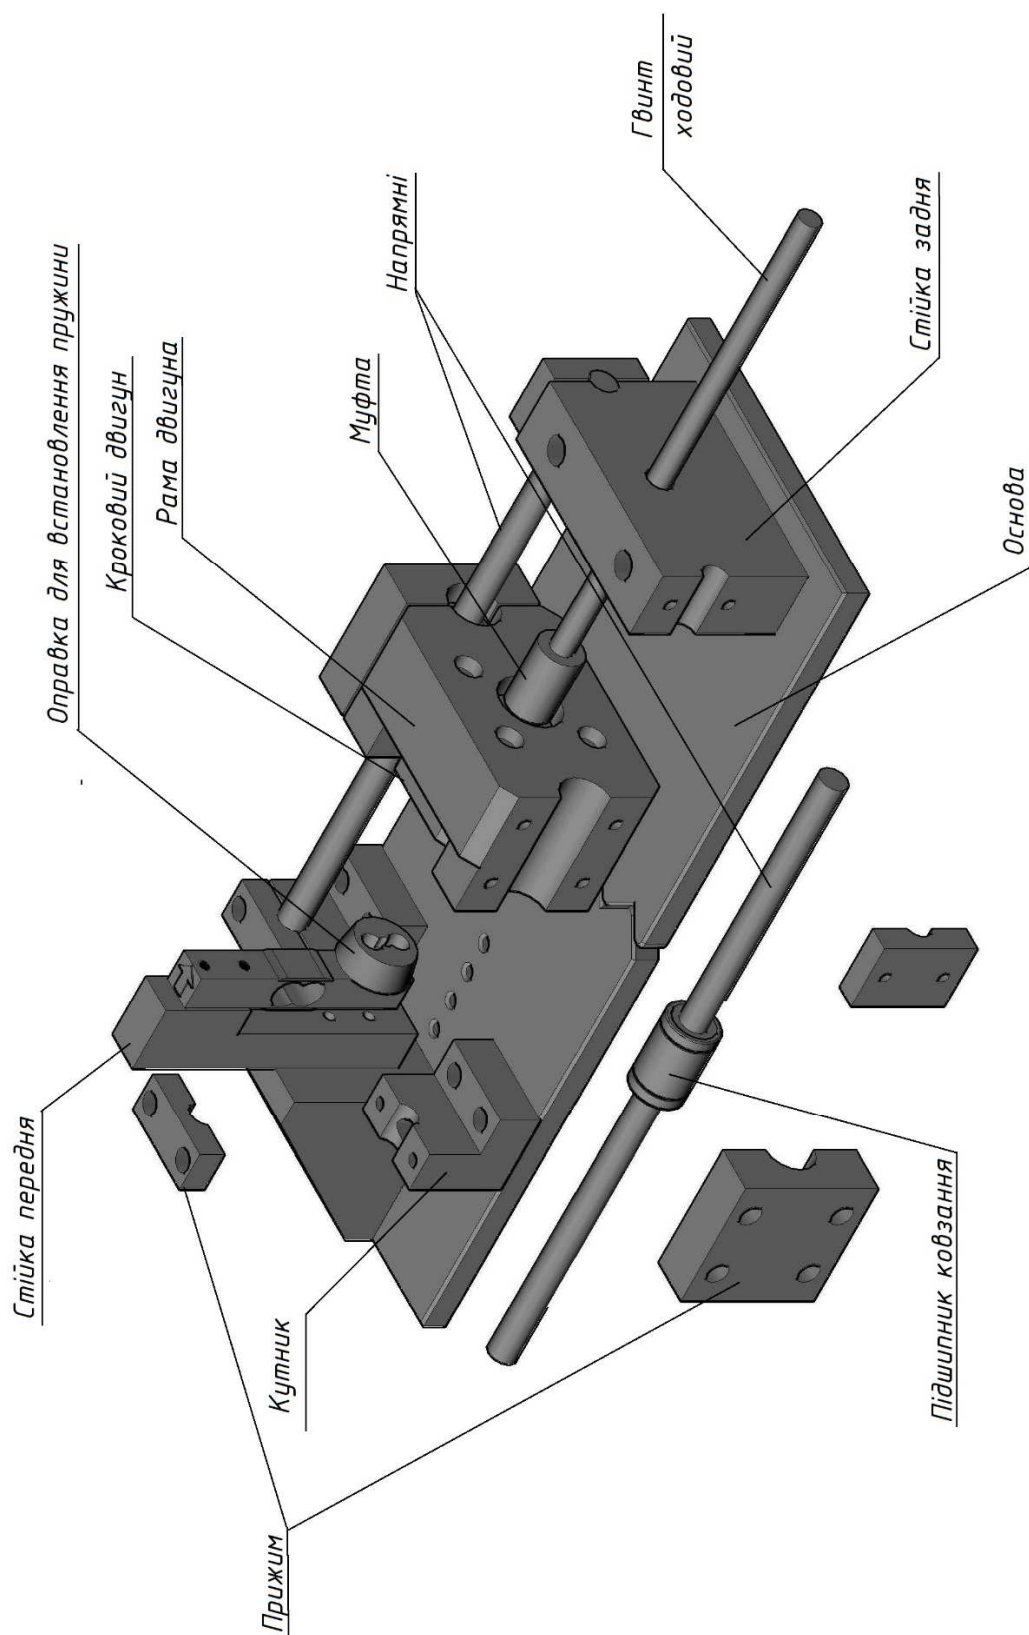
Конструкція автоматизованого лабораторного стенду для тестування пружин стиснення
